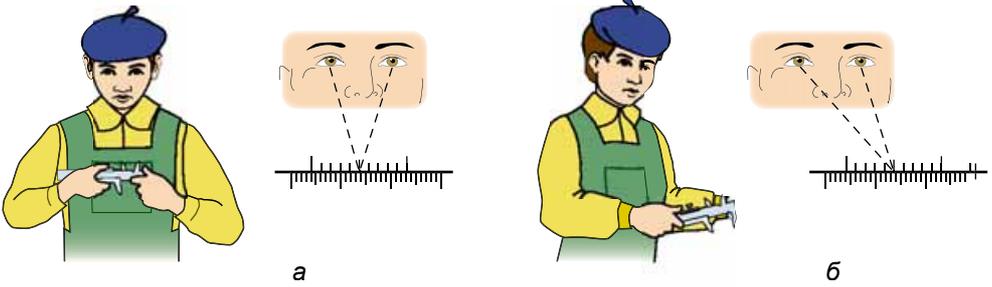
Вимірювання і контроль розмірів деталей штангенциркулем ШЦ-I:
